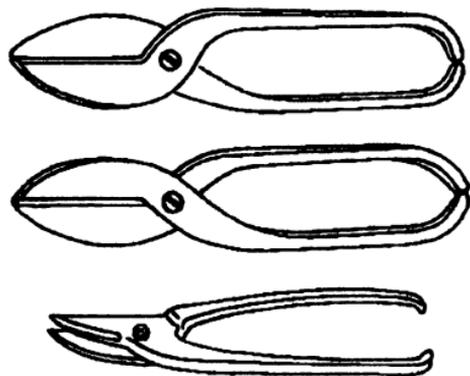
Ножницы для резки тонкого листового металла:
